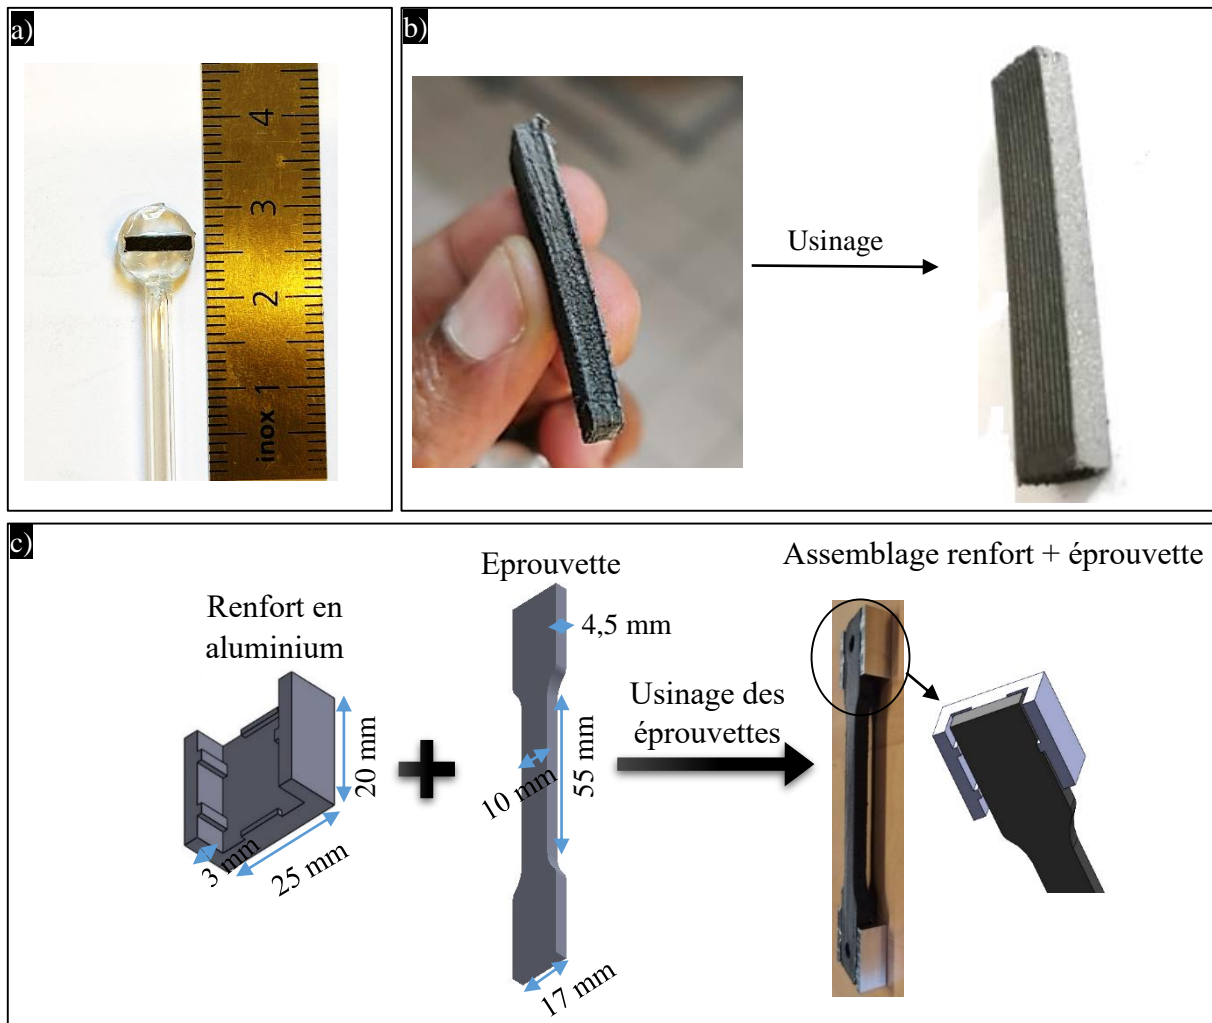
Post traitement des éprouvettes de : a) éprouvette imprimée mis dans le dispositif de mesure VSM ; b) éprouvette imprimée usinée pour essai de flexion 3 points ; c) éprouvette imprimée usinée équipée de ses renforts métalliques pour les essais de traction
